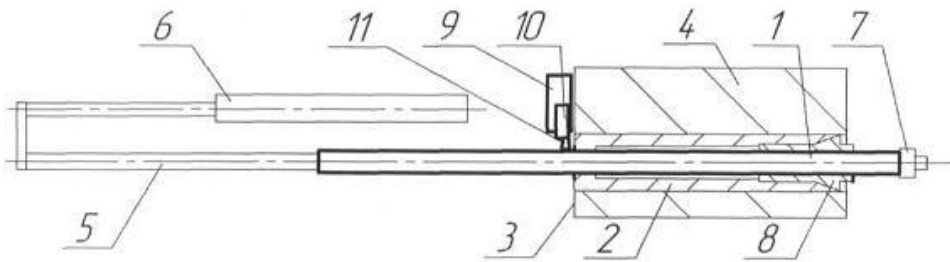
Спосіб завантаження металорізального верстата прутком: пруток 1; шпиндель 2; задня сторона 3 шпиндельної бабки 4; шток 5 пристрою 6 для завантаження; упор 7; затискний пристрій 8; відрізний супорт 9; різцетримач 10; відрізний різець 11
